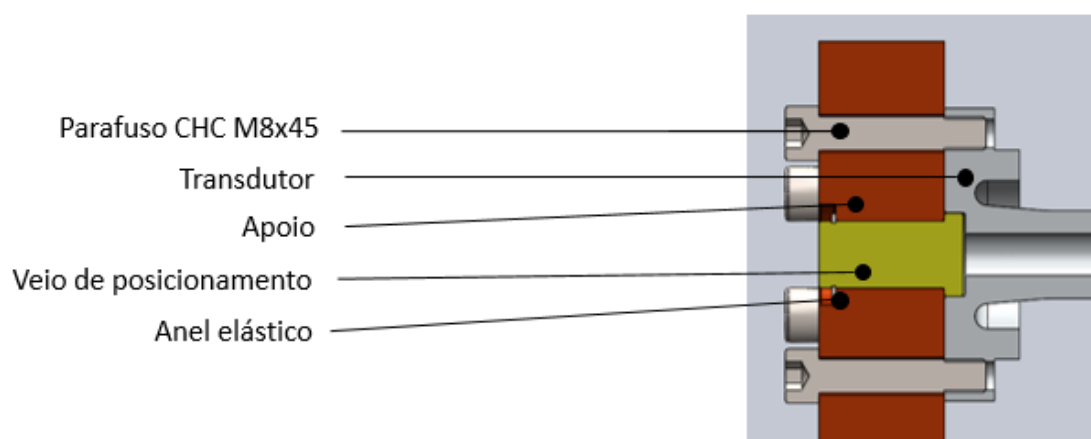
Pormenor da ligação do transdutor ao apoio [2]
